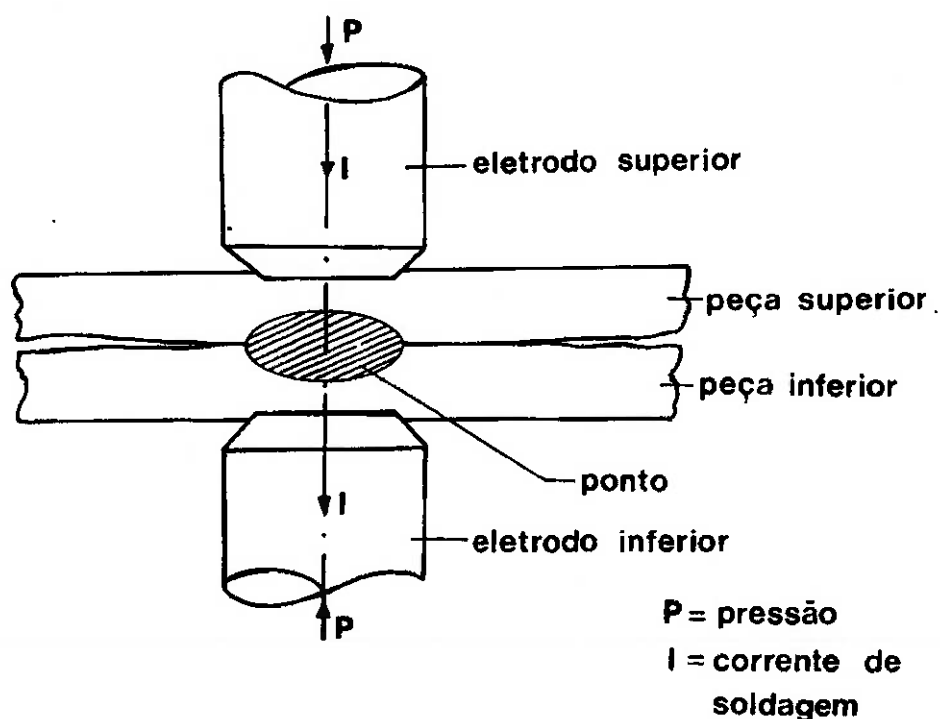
2 - Esquema básico da soldagem por resistência. [2]
